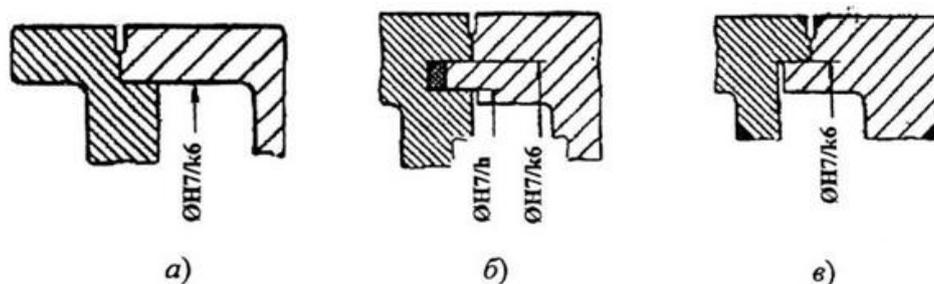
Конструкции стыков корпусов секций насоса
